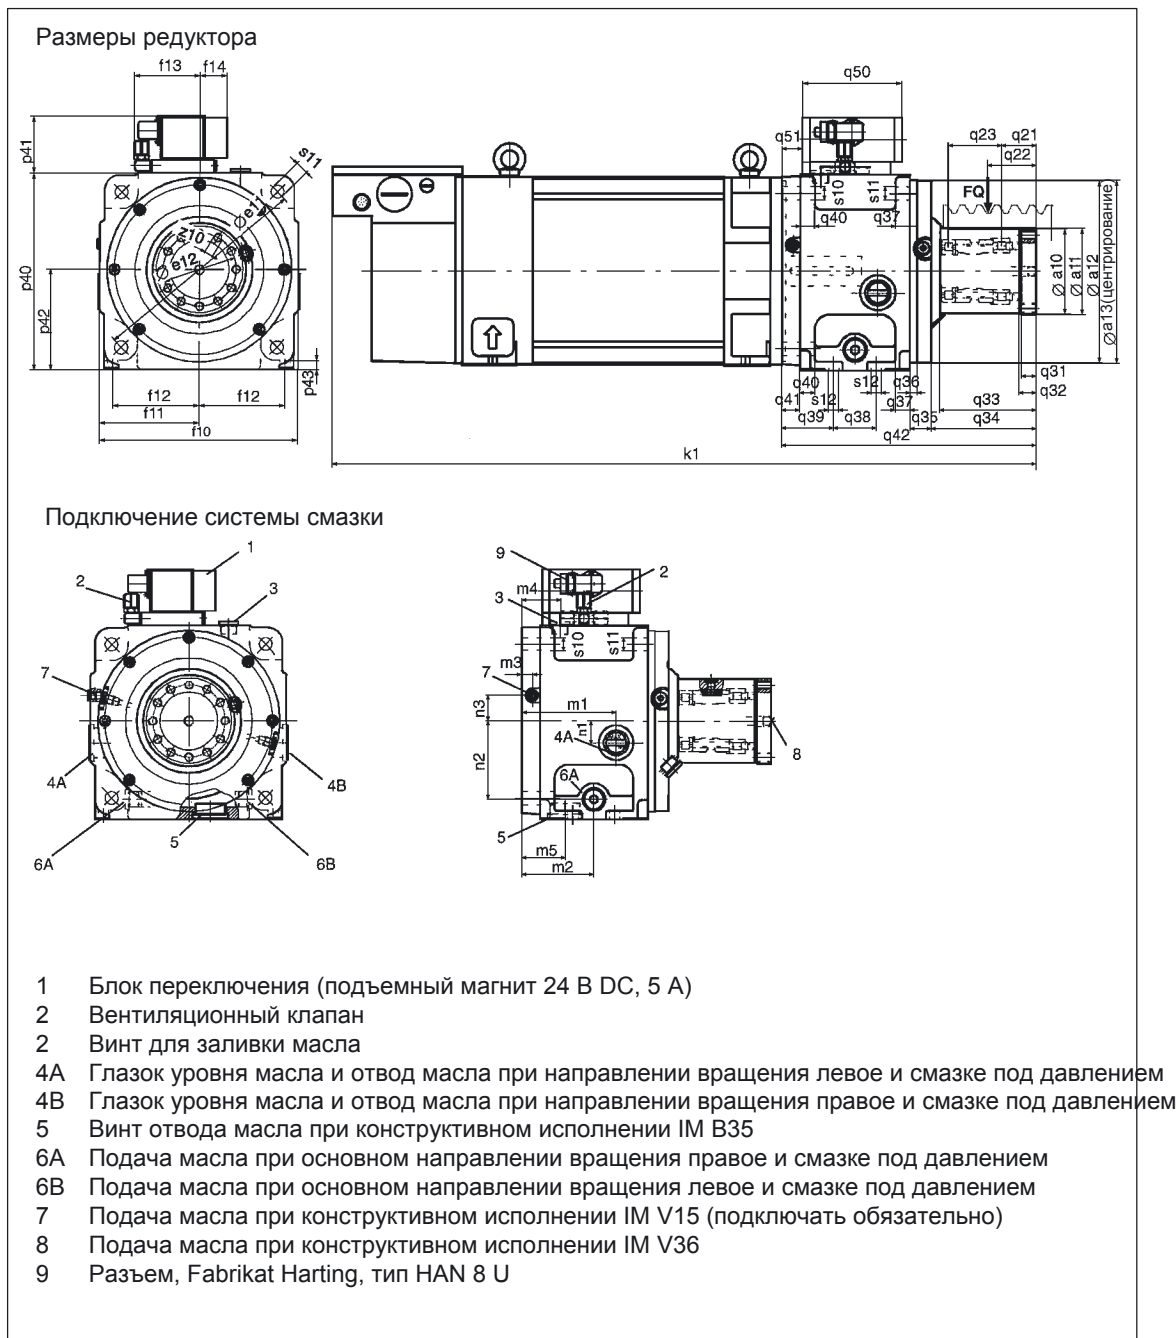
Двигатель трехфазного тока и размеры редуктора
